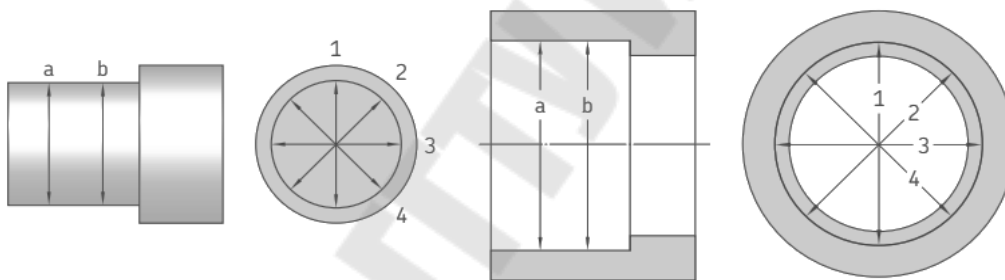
Контроль диаметра вала и посадочных поверхностей корпуса
